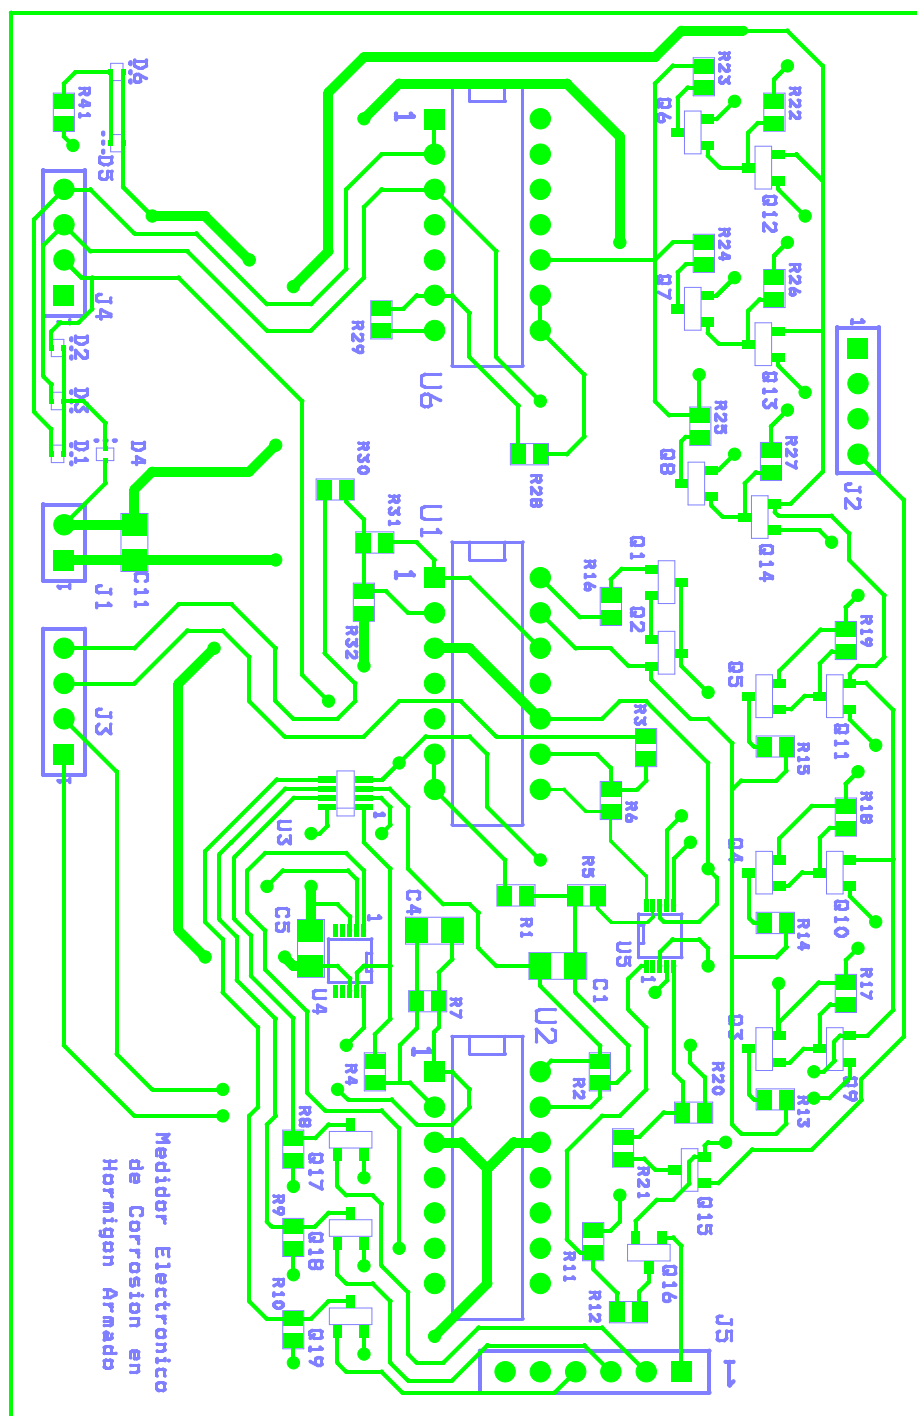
Vista superior del PCB de la etapa de I/O de MECCHA.
